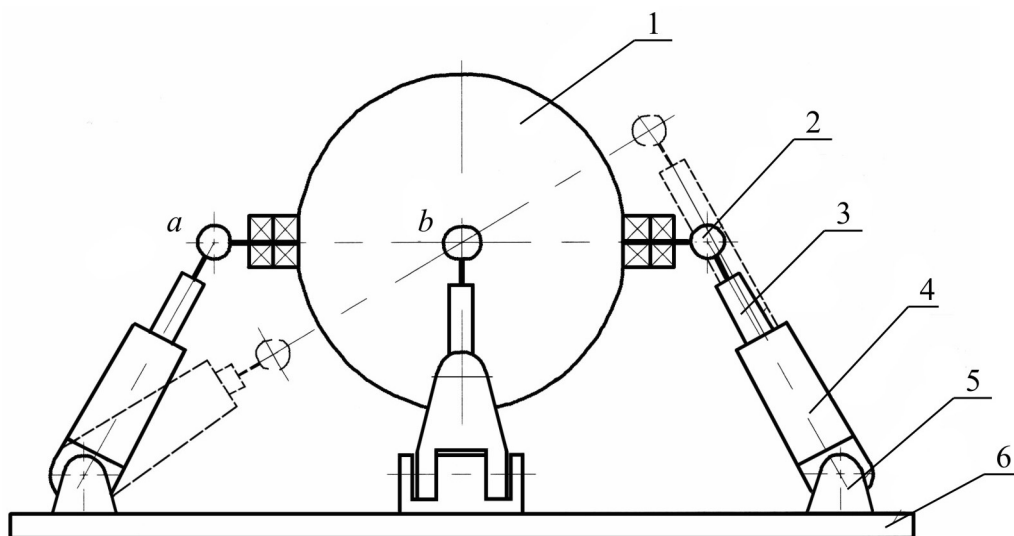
Гиросtabilизатор с линейными приводами поворота
